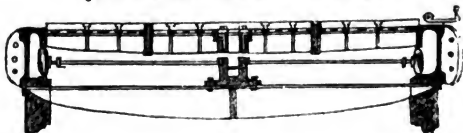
Coupe verticale passant par l'axe de l'appareil.
